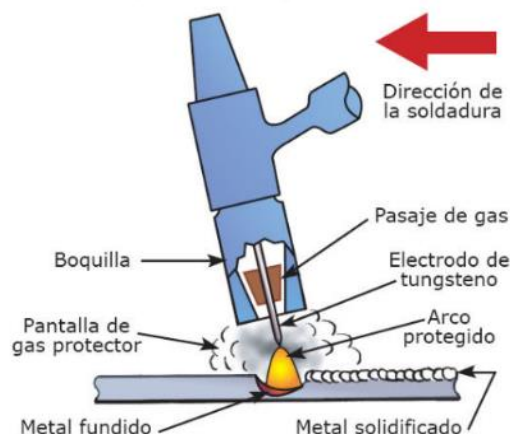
Representación de la soldadura por GTAW/TIG
